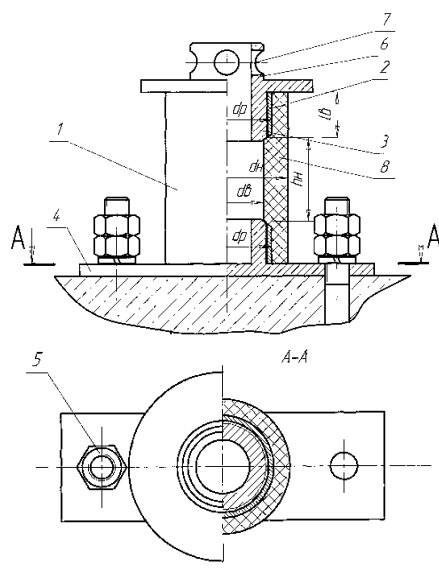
Цилиндрическая упругая опора: 1 — корпус, 2 — верхнее основание, 4 — нижнее основание, 5 — болтовое соединение, 6 — выступ; 7 — технологическое отверстие; d_p — диаметр резьбы втулки, l_v — ширина втулки, d_n — наружный диаметр сплошного корпуса, d_v — внутренний диаметр сплошного корпуса, h_n — рабочая высота сплошного корпуса
